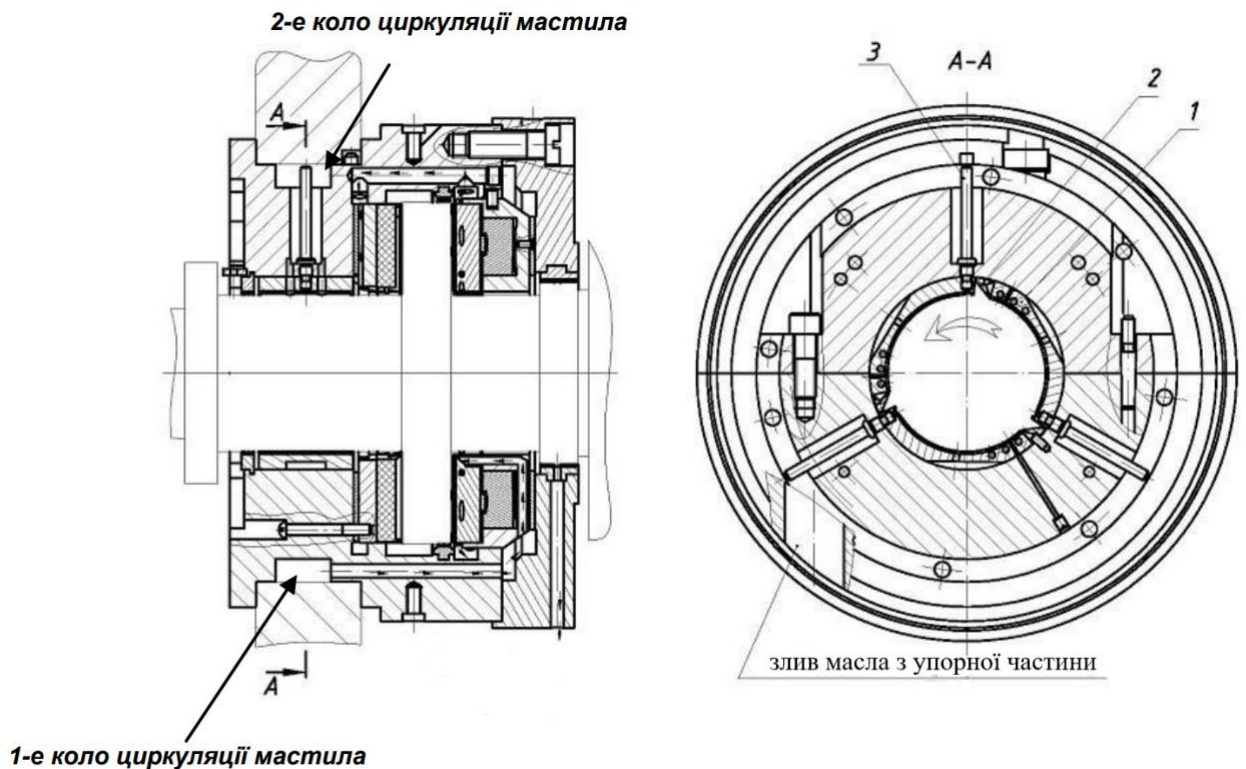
Підшипник опорно-упорний з двома колами циркуляції мастила [11]
